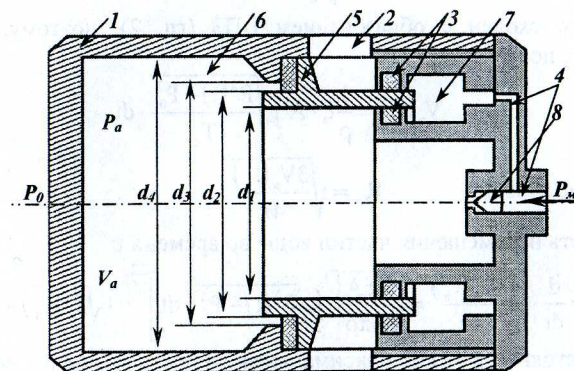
Принципиальная схема ПИ энергетического воздействия: 1 – цилиндрический корпус; 2 – выхлопные окна; 3 – уплотнительные кольца; 4 – воздуховодный канал; 5 – фигурный поршень; 6 – рабочая камера; 7 – подпорная камера; 8 – регулировочный дроссель.
